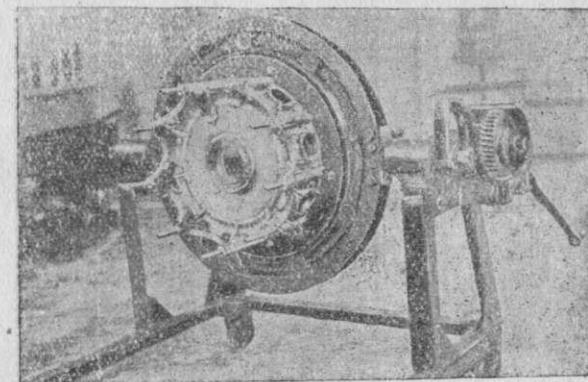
Поворотный станок для сборки звездообразных моторов.
